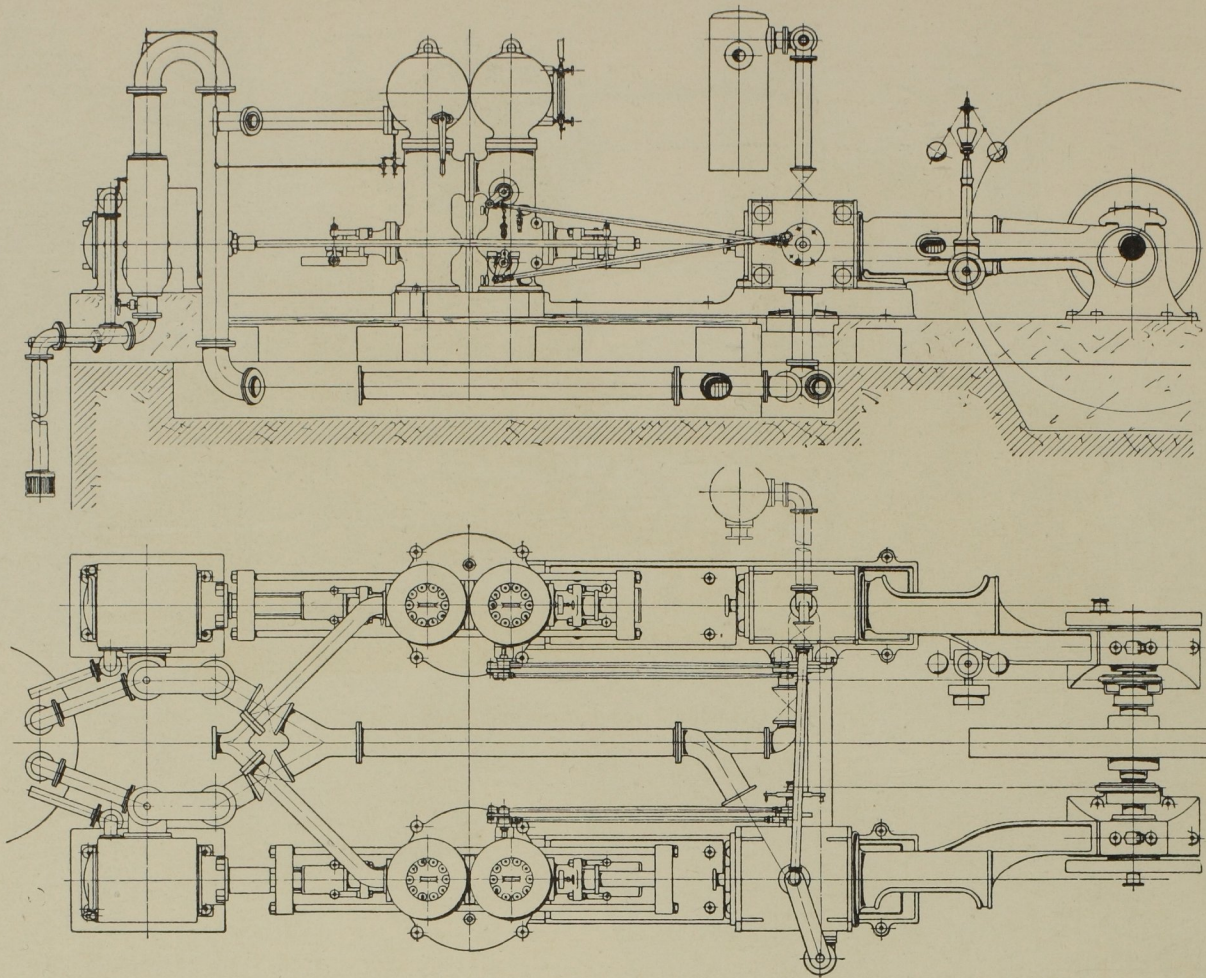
Seitenansicht und Grundriss. Masst. 1:64.
